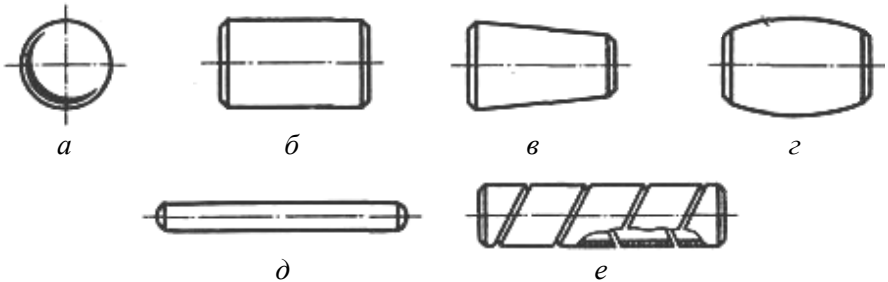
Виды тел качения: а) шарик; б) цилиндрический; в) конический; г) бочкообразный; д) игольчатый; е) витой
